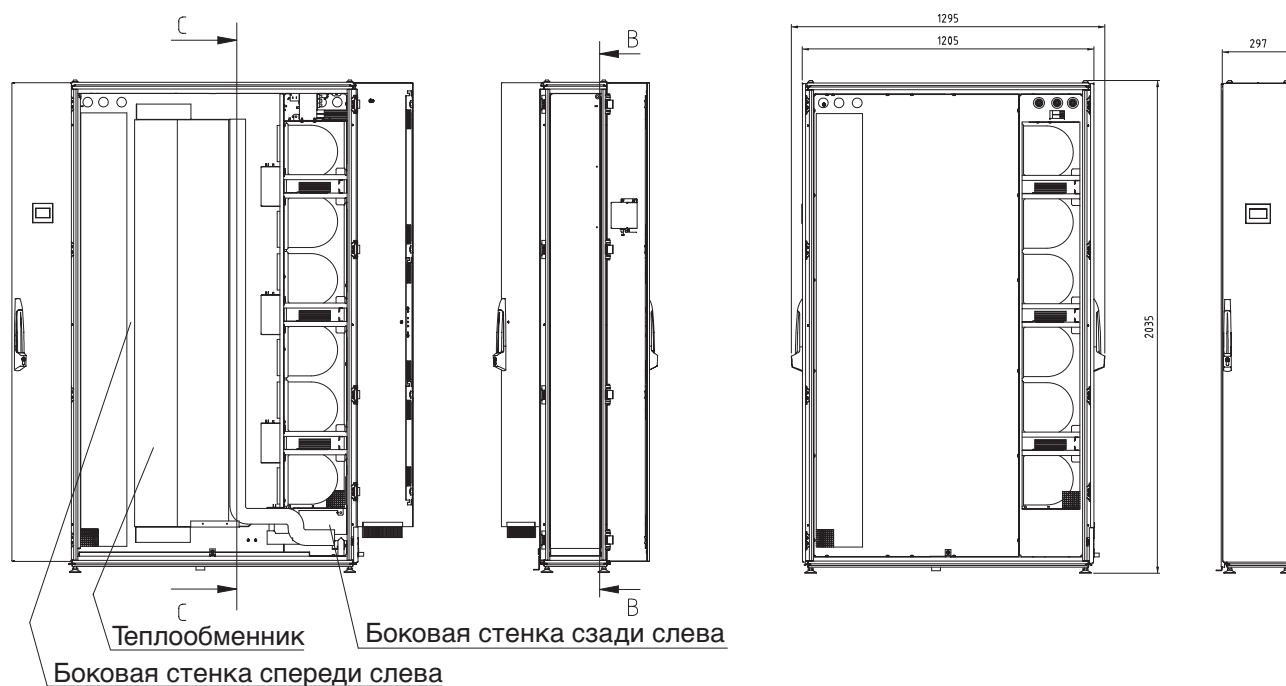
Обзорный чертеж – Liquid Cooling Package Plus EC (передняя, задняя, боковая стороны)
